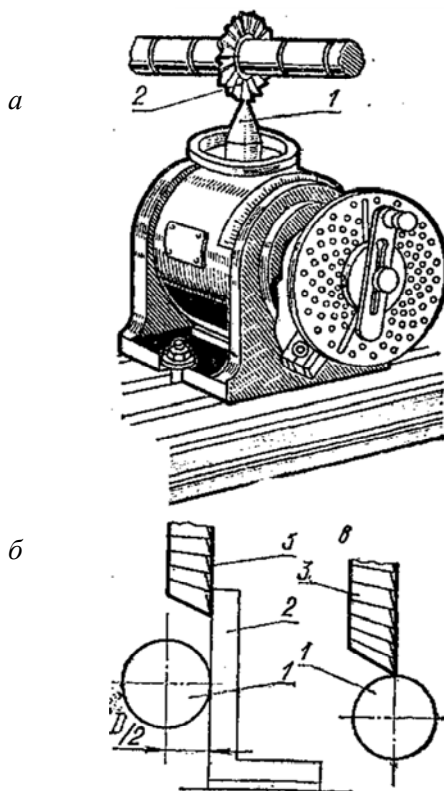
Установка дисковой фрезы в диаметральной плоскости заготовки
